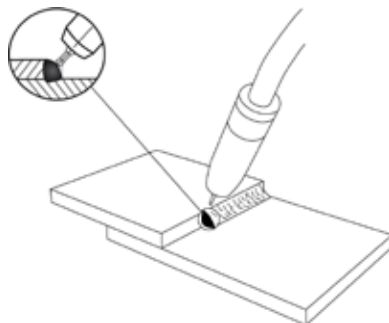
Вылет сварочной проволоки.
